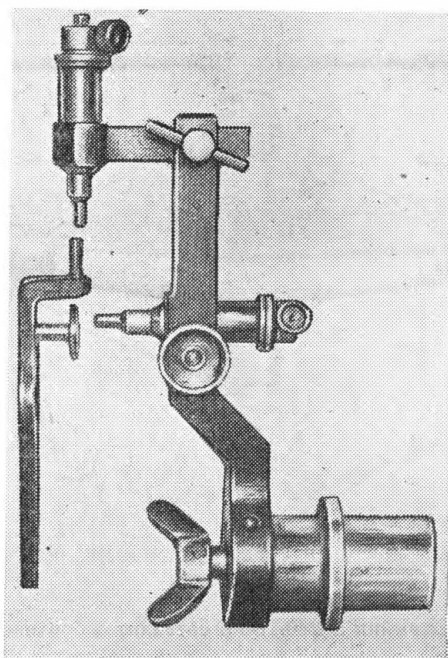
Приспособление Т-9578-441 для центровки коробки передач по двигателю
